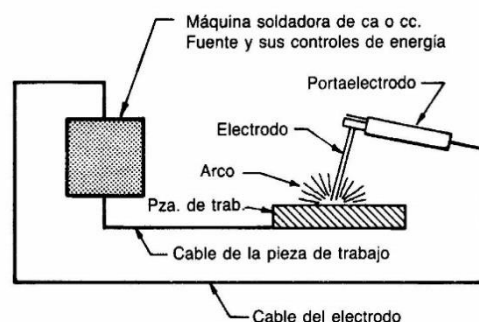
Componentes básicos de la soldadura por arco
